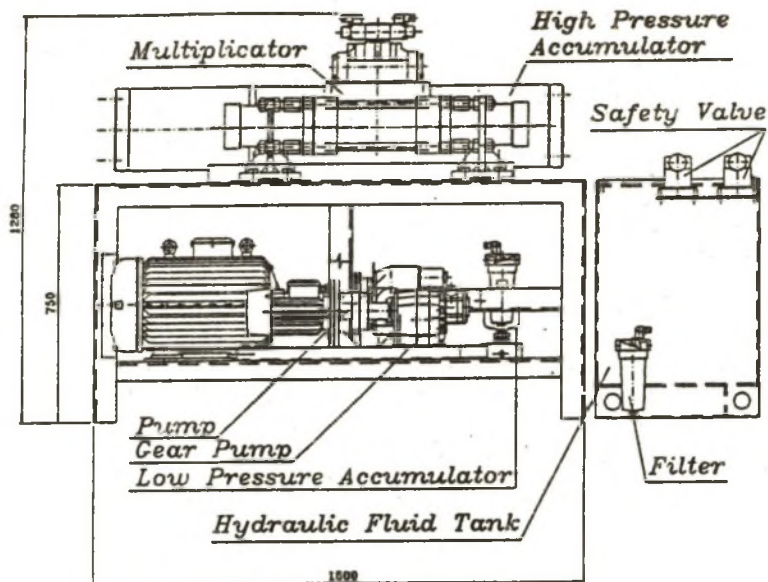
Konstruktionsschema des Hochdruckwasserübersetzerpumpe
